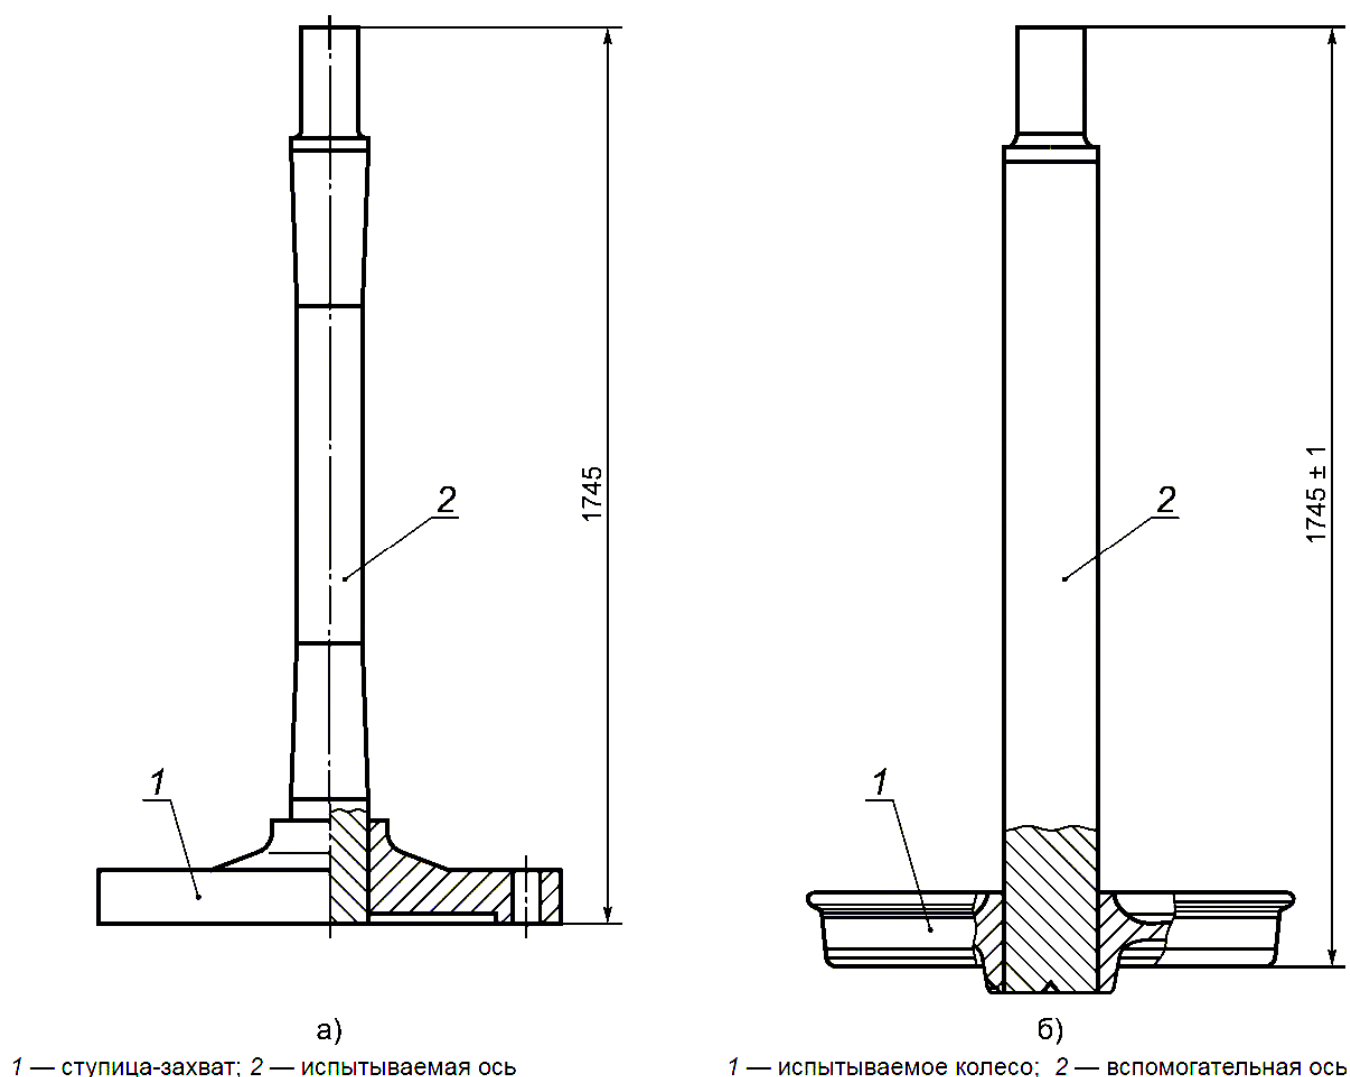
Примеры образцов оси и колеса для испытаний на усталость.
